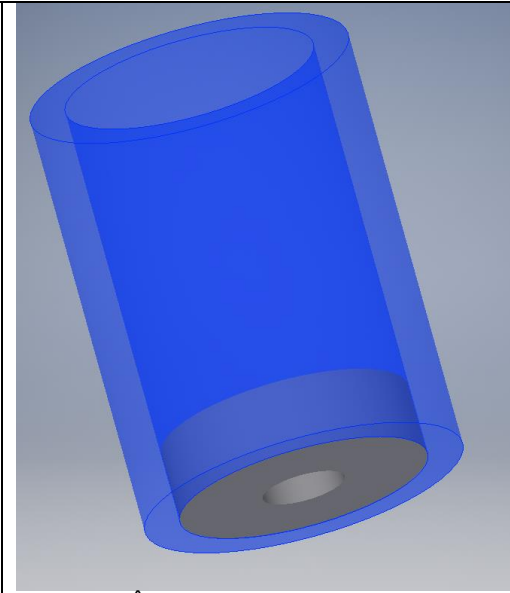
Îmbinare placa de bază cu corpul matriței tubulare
